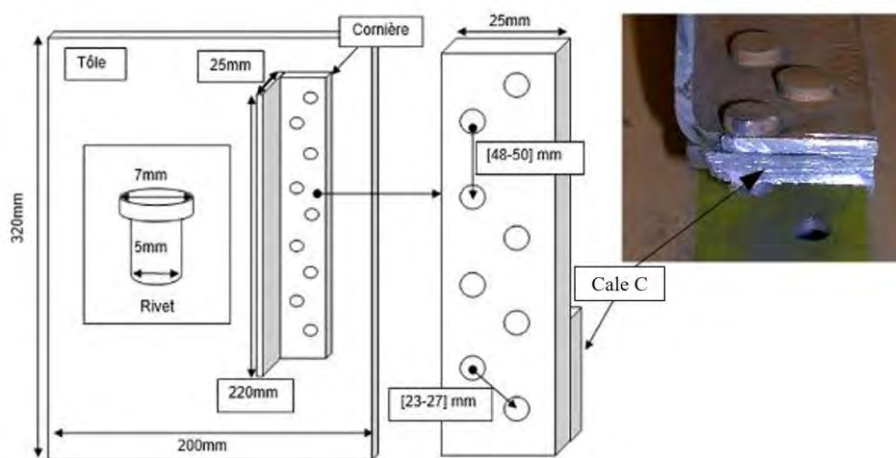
Schéma situant la zone de prélèvement et photo de la cale C de l'assemblage L2
